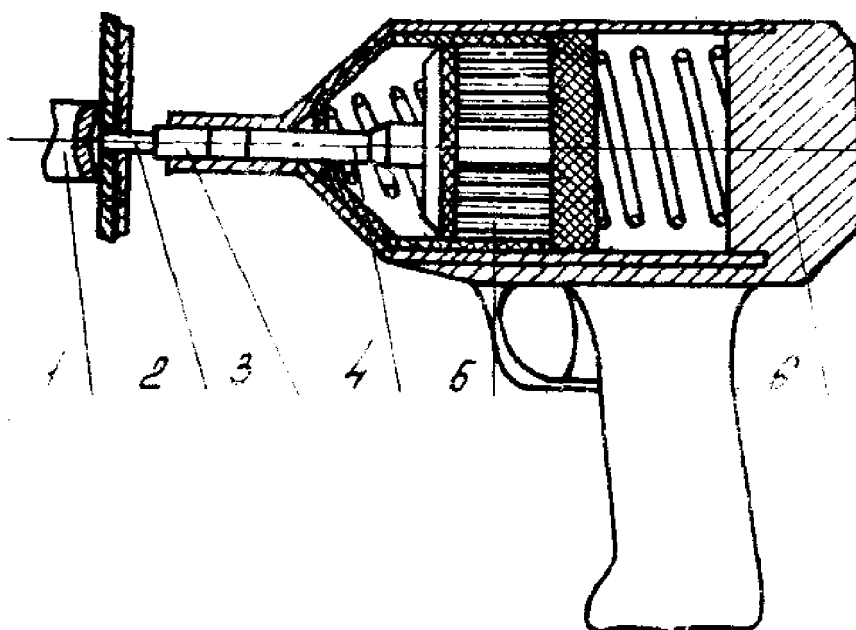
Схема клепки магнитно-импульсным клепальным молотком: 1-поддержка; 2-заклепка; 3-обжимка; 4-боек; 5-индуктор; 6-корпус
